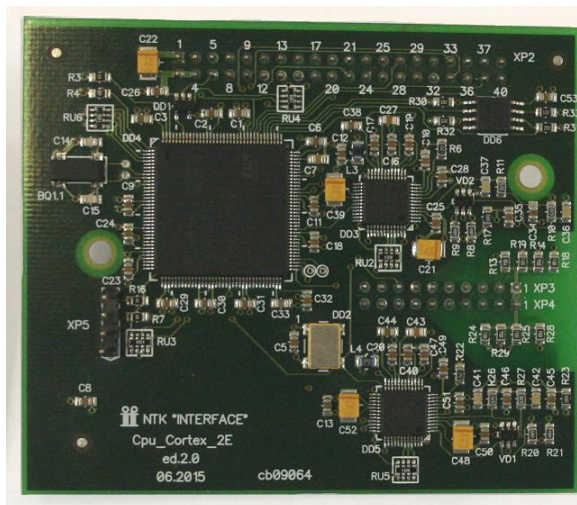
Внешний вид процессорного модуля контроллера «Синком-Д»
